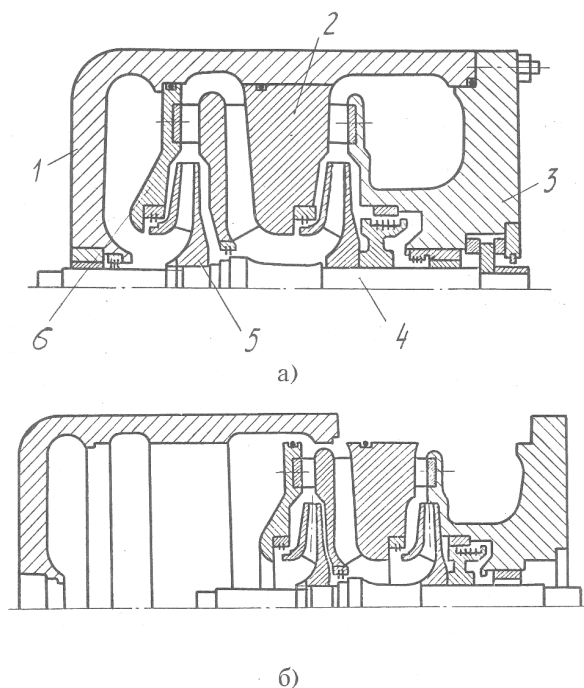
Двухступенчатый нагнетатель с аэродинамическим узлом на крышке: а, б — соответственно в собранном и разобранном видах; 1 — корпус; 2 — пакет элементов проточной части; 3 — крышка; 4 — ротор; 5 — съемное РК; 6 — неразъемная мембрана. Силовой корпус 1 типа «баррель» не имеет горизонтального разъема (корпуса с горизонтальным разъемом не обеспечивают прочности при давлениях более 3 – 4 МПа.)
